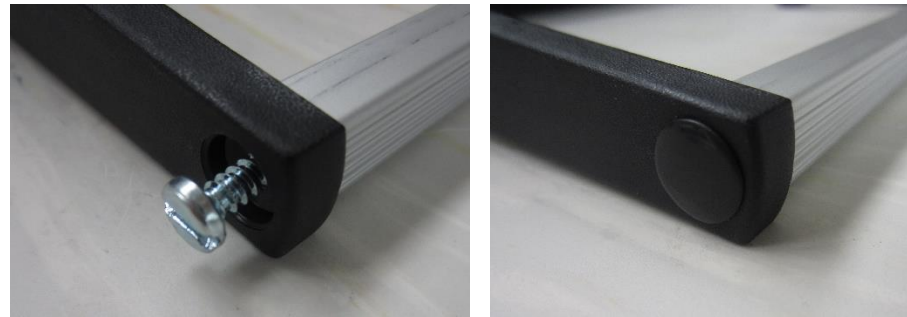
Profilschraube C (links), Stopfen D (rechts)
